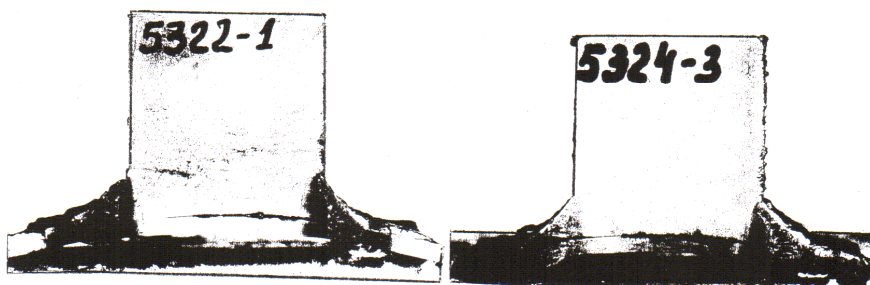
Микрошлифы сварных образцов, \times^5
